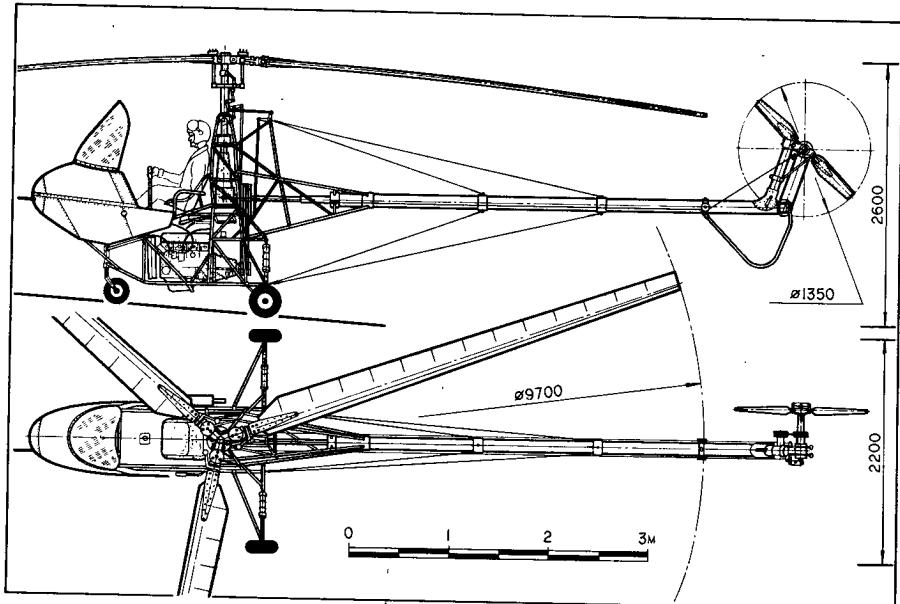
Вертолет «Горник-4» Н. Демидова (Новошахтинск), 1984 г. Удостоен высшей награды на слете СЛА-85 в Киеве. Автомобильный двигатель ВАЗ-2103 мощностью 75 л. с., обороты двигателя — 5000 об/мин, обороты несущего винта — 280 об/мин, диаметр несущего винта — 9,7 м, лопасти от вертолета Ка-26 с обрезанной кромкой частью, взлетная масса вертолета — 500 кг, масса пустого — 394 кг, максимальная скорость — 150 км/ч, крейсерская — 120 км/ч
